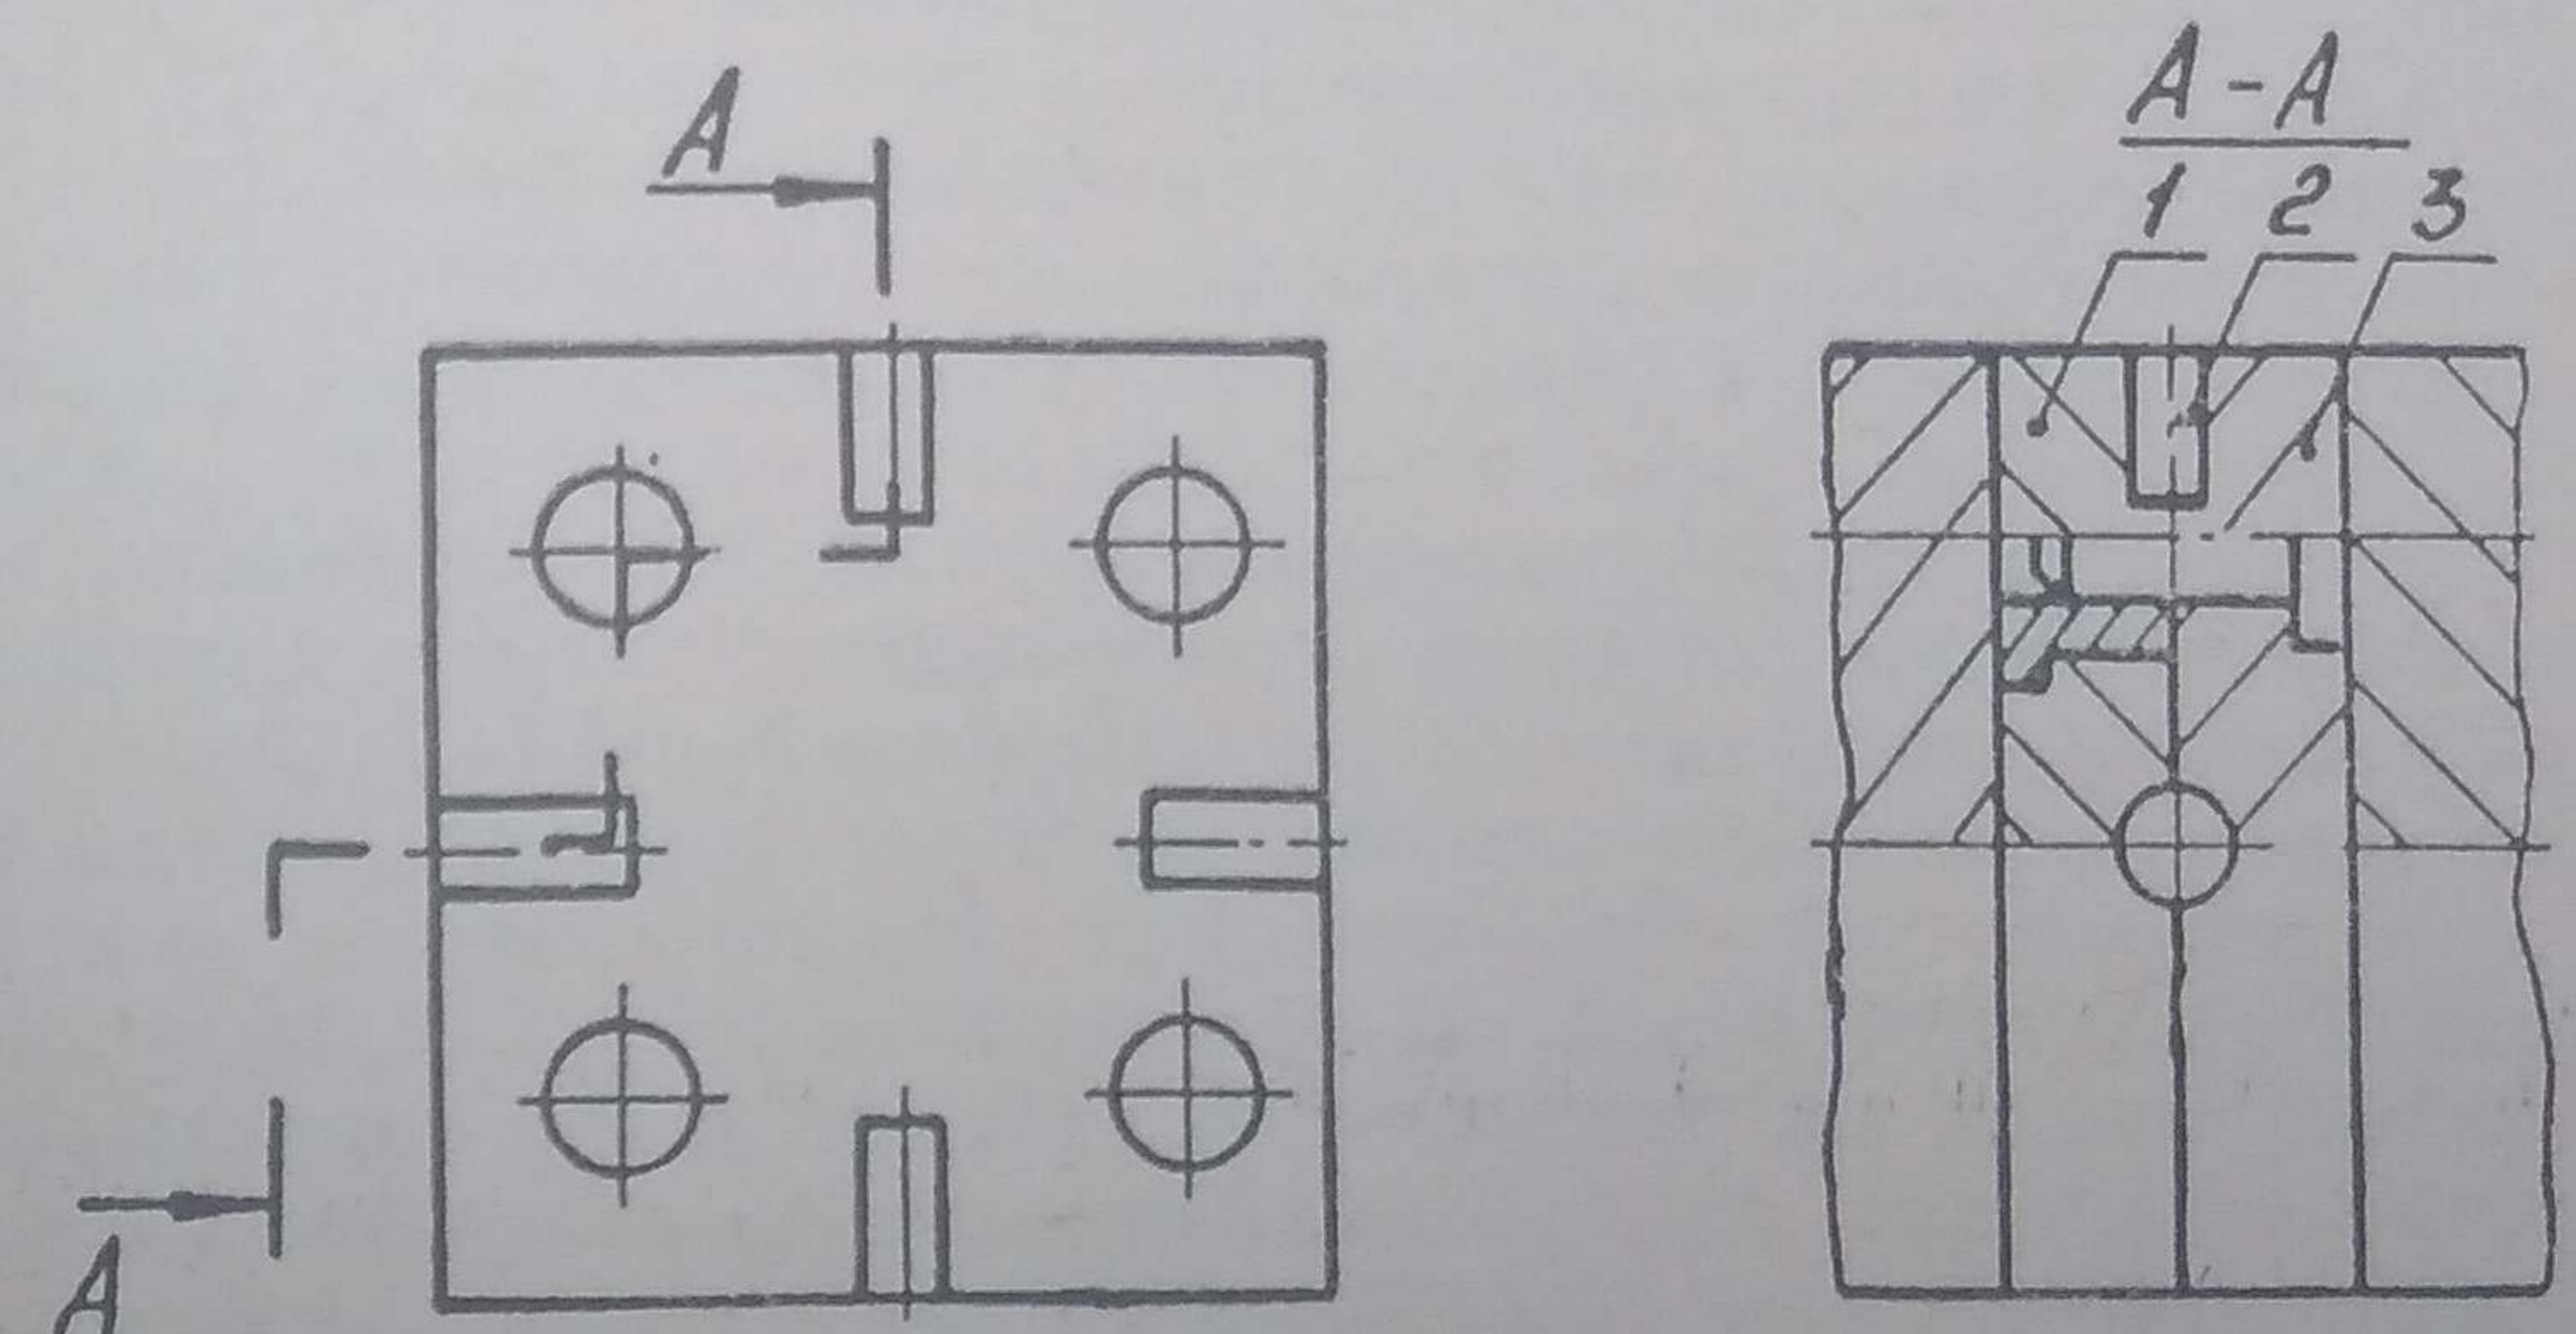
Узел центрирования полуформ цилиндрическими поверхностями параллельными плоскостями разреза:
